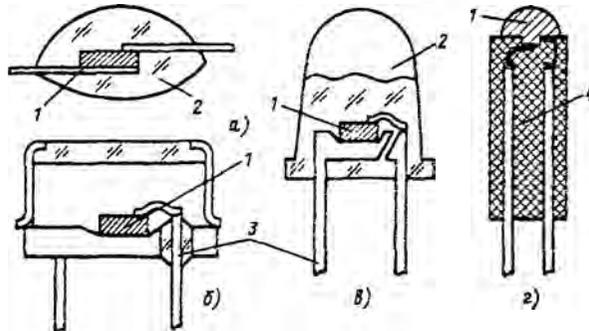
Конструкции некоторых типов СИД: а – бескорпусный; б – в металлостеклянном корпусе; в – с полимерной линзой в полимерном корпусе: 1 – кристалл; 2 – полимерная защита; 3 – ножка; 4 – полимерный корпус
